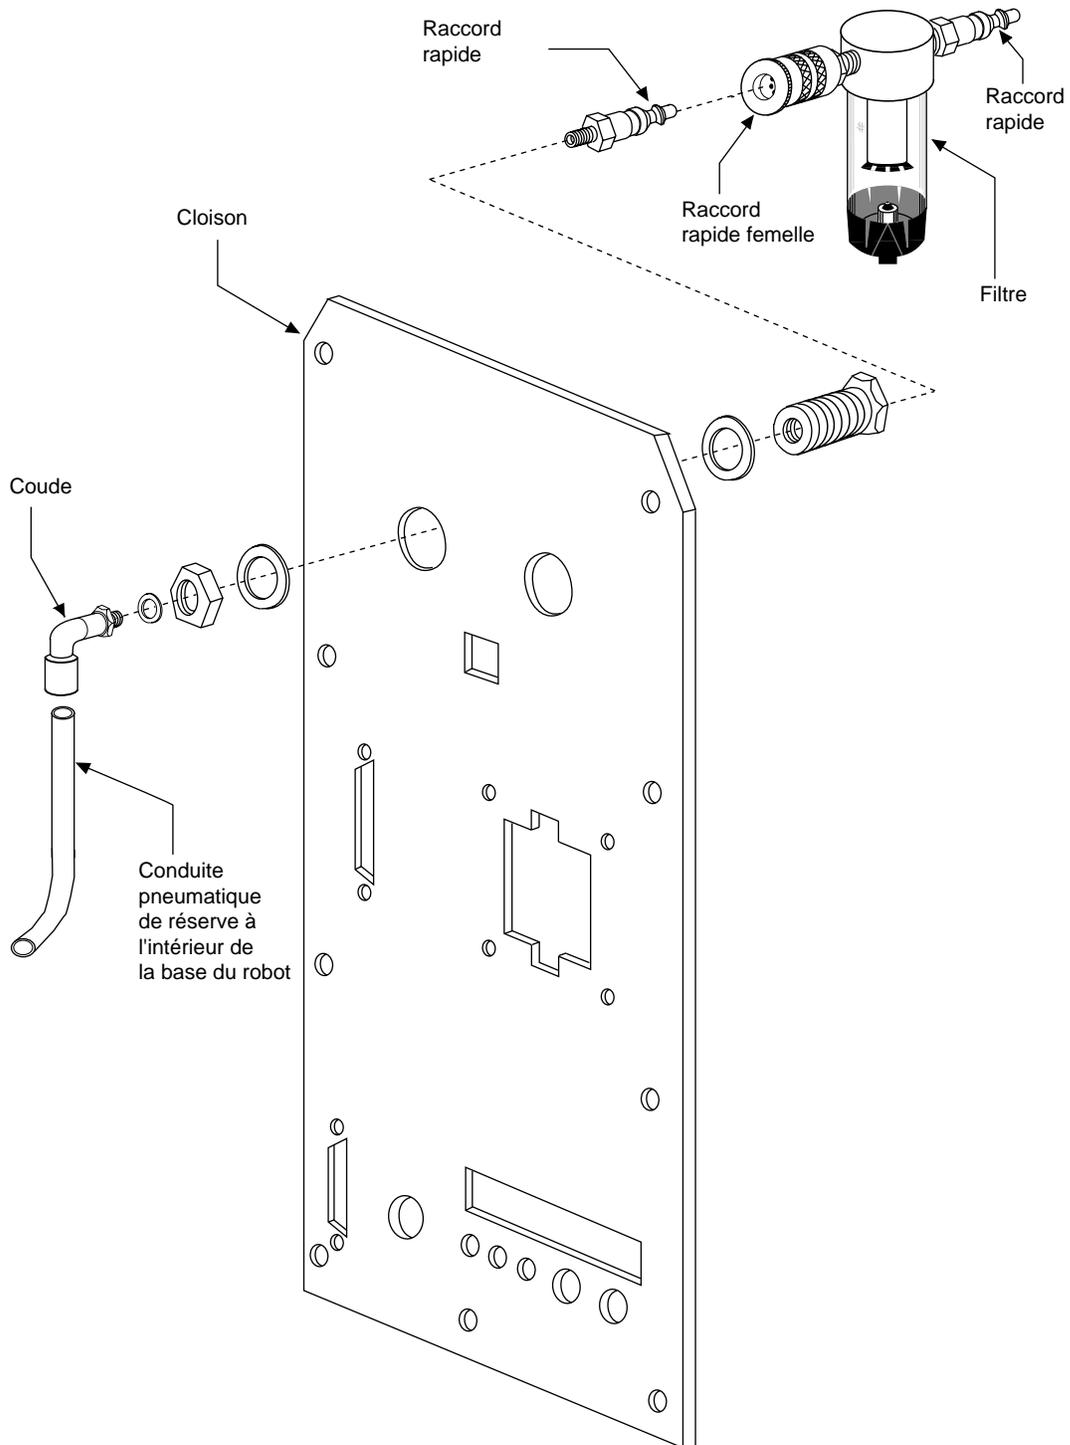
Ensemble de filtre à air du robot Cobra 600
